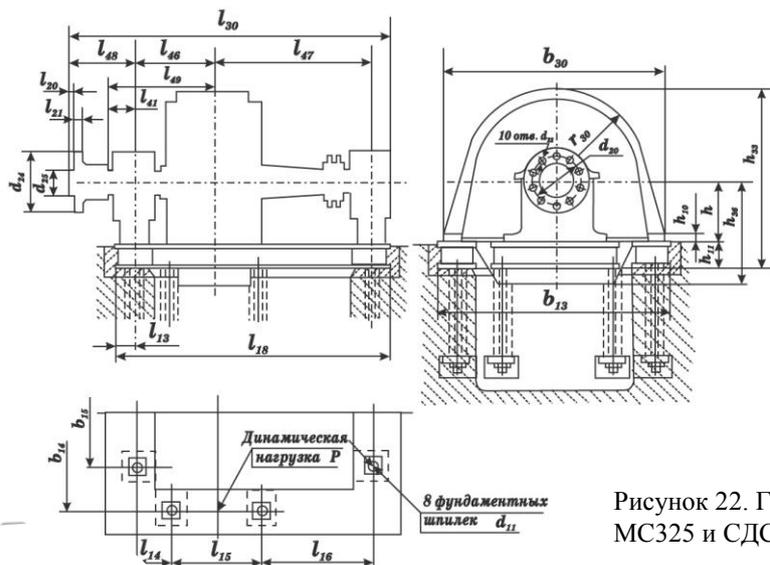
Габаритные размеры МС325 и СДСЗ-290
